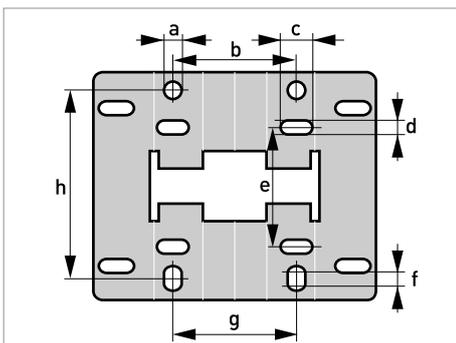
Abmessungen der Montageplatte für das Wandgehäuse
